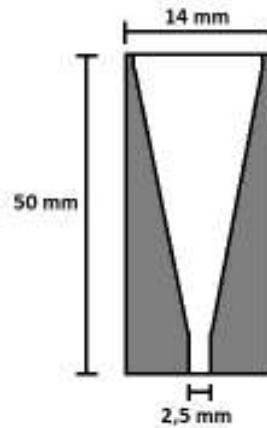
Desenho dimensional do dispositivo utilizado para regular vazão de partículas.
